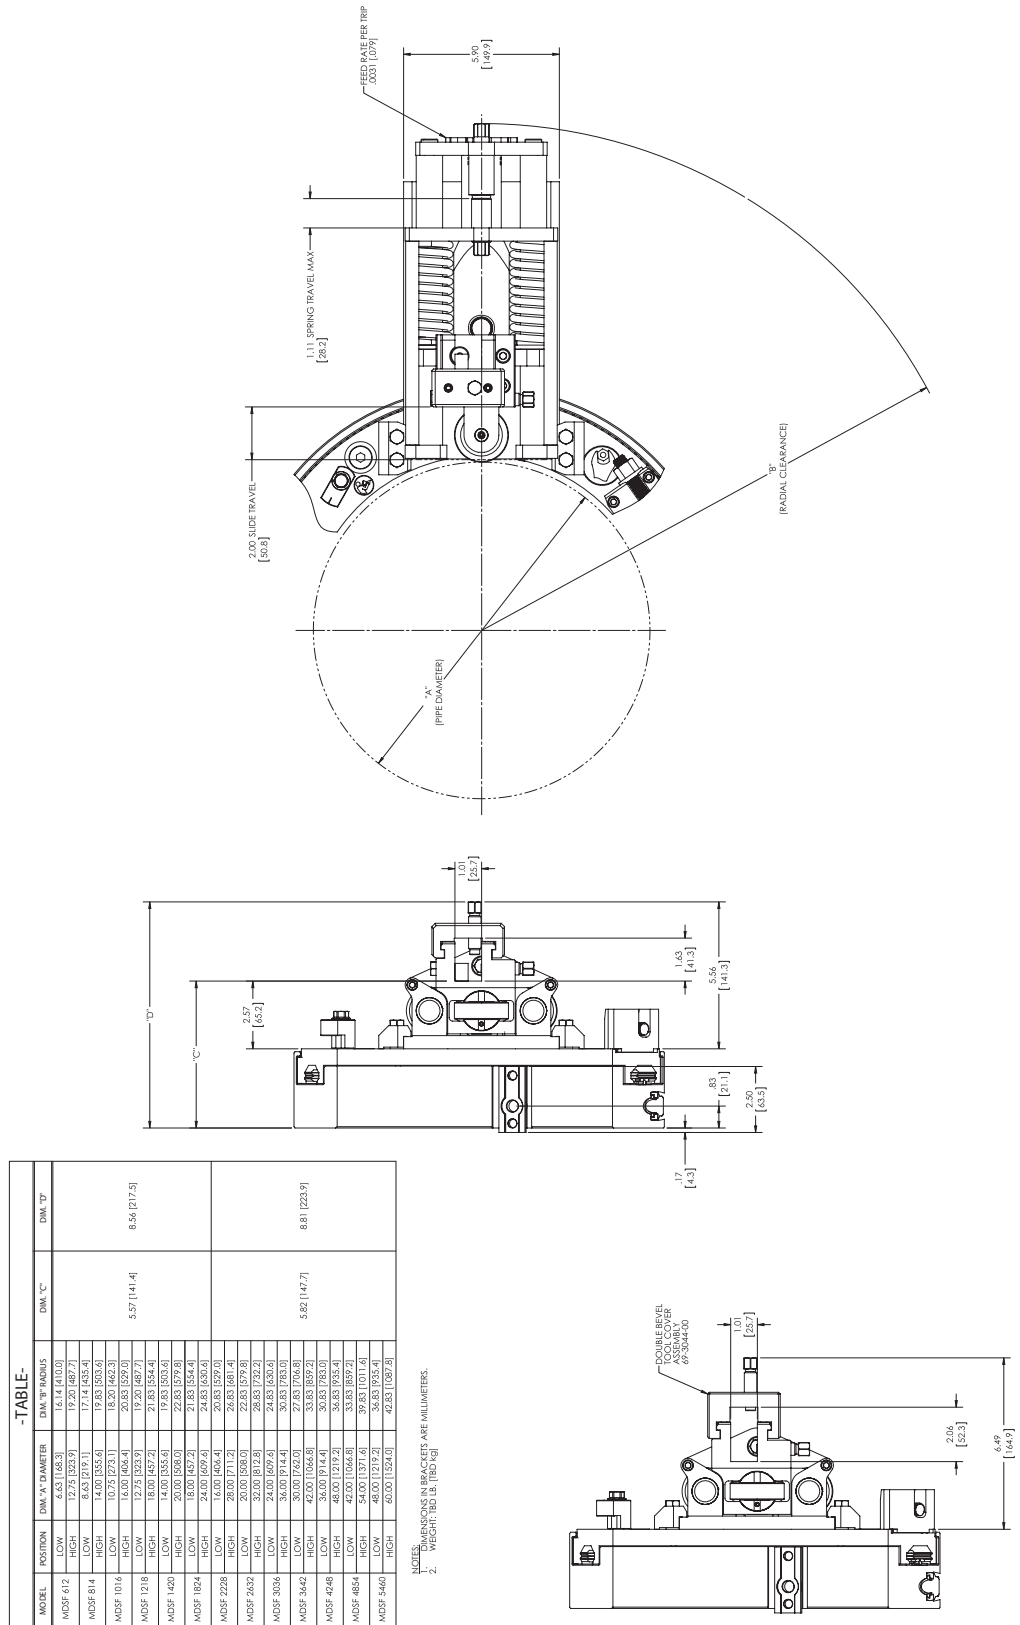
Les dessins représentent les dimensions opérationnelles des plateaux pour toutes les dimensions de machines.
